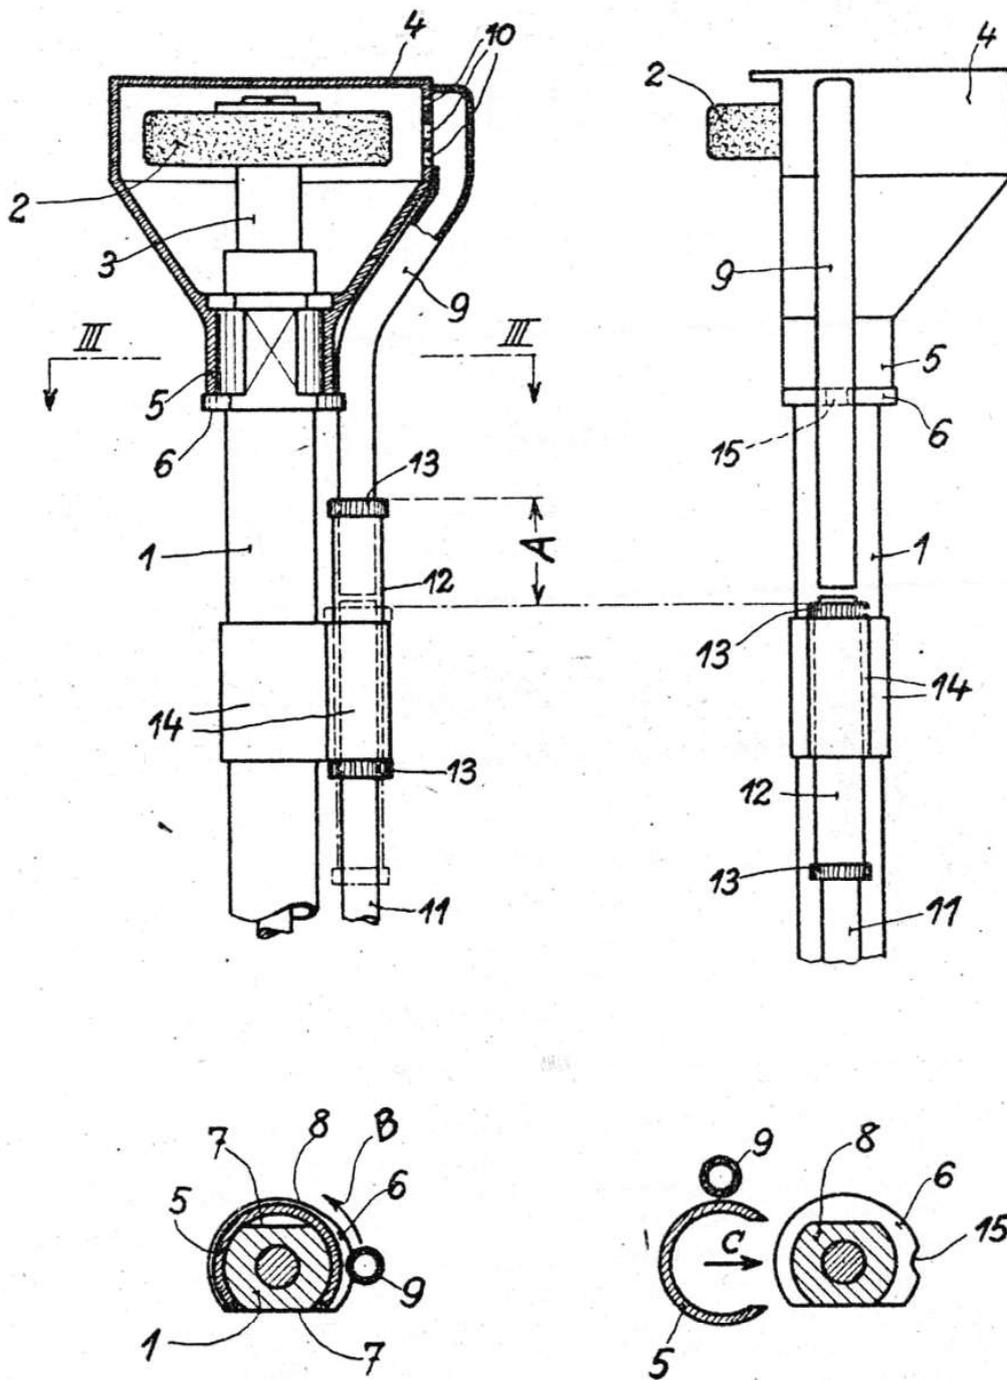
Detailzeichnung des geraden Handstücks (links oben: Schleifvorrichtung, teils in Ansicht, teils im Mittelschnitt; rechts oben: Seitenansicht; links unten: Grundriß nach der Schnittlinie III-III; rechts unten: Grundriß nach der Schnittlinie III-III, vor dem Aufsetzen der Schutzkappe)
